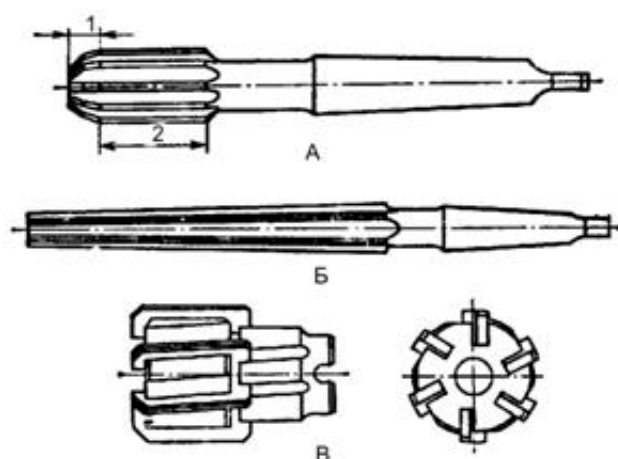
Развертки: А — цилиндрическая; Б — коническая; В — машинная насадная;
